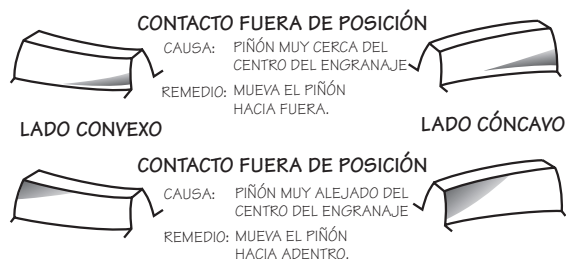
Patrón de los dientes del engranaje cónico con dentado helicoidal
